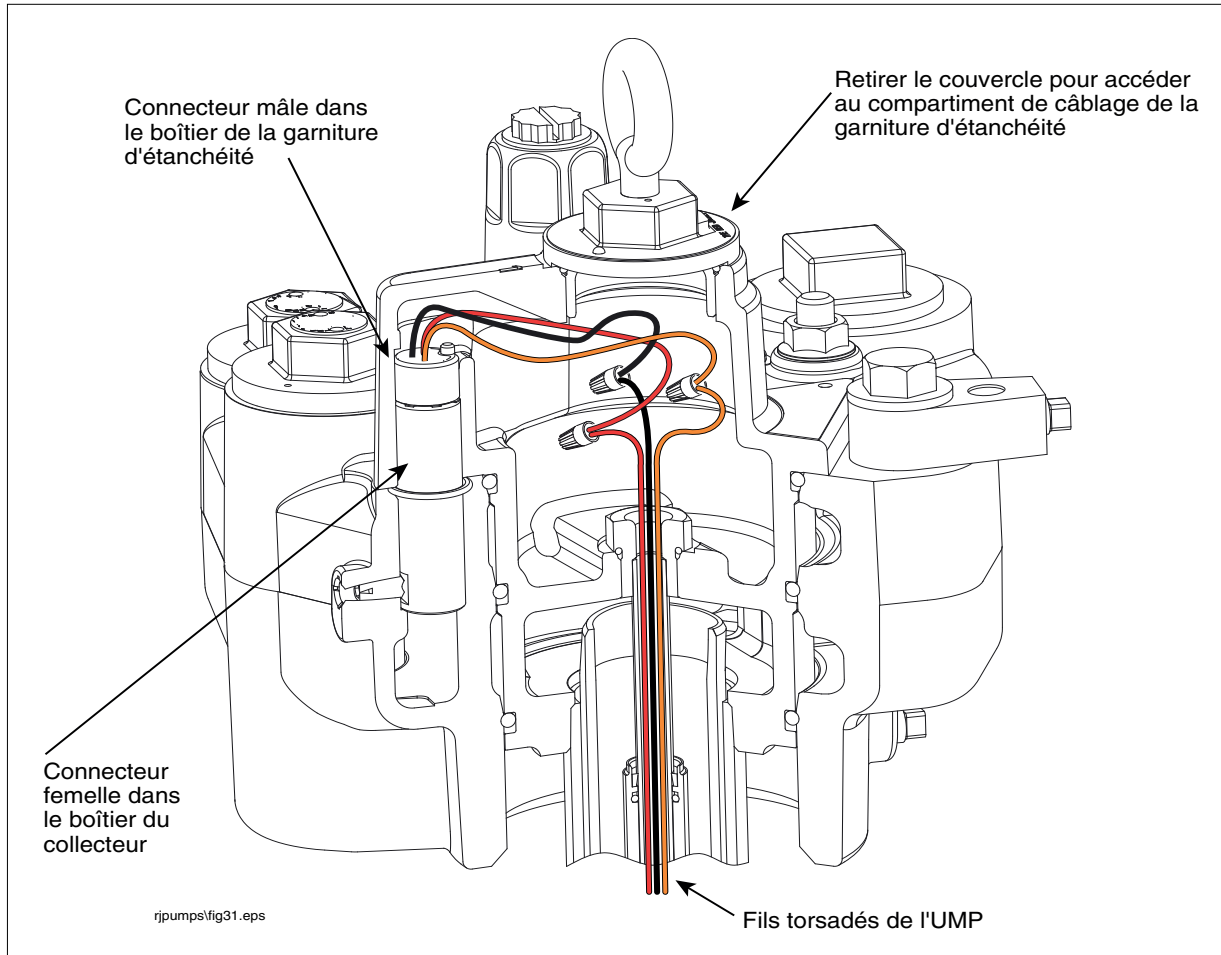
Raccordement de l'UMP au câblage de la garniture d'étanchéité
